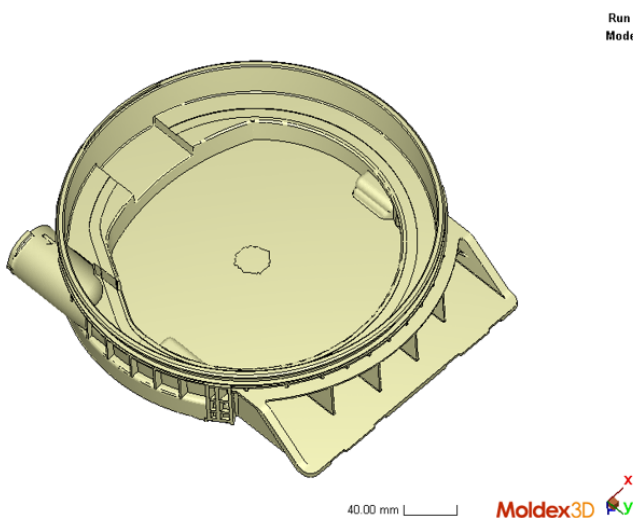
Geometria CAD del componente importata su Moldex3D.
